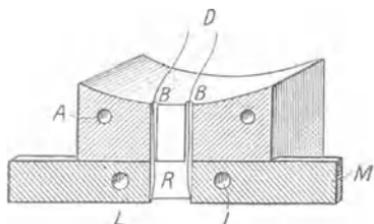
Sockel im Schnitt durch die Ebene der Kontaktmesser.
